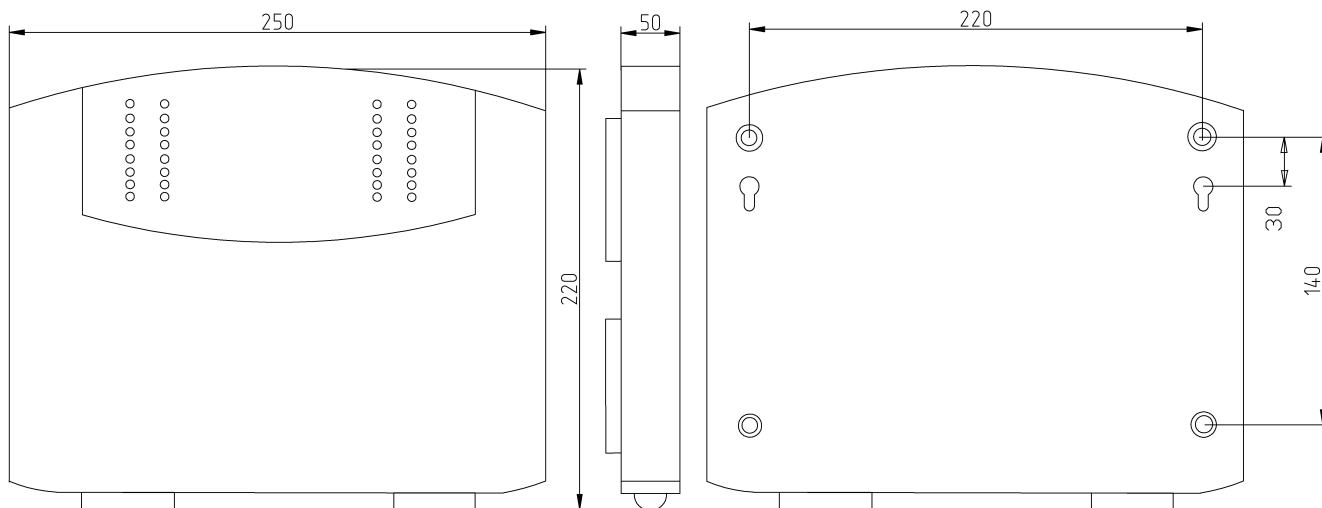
Габаритные и установочные размеры прибора (пластиковый корпус)
